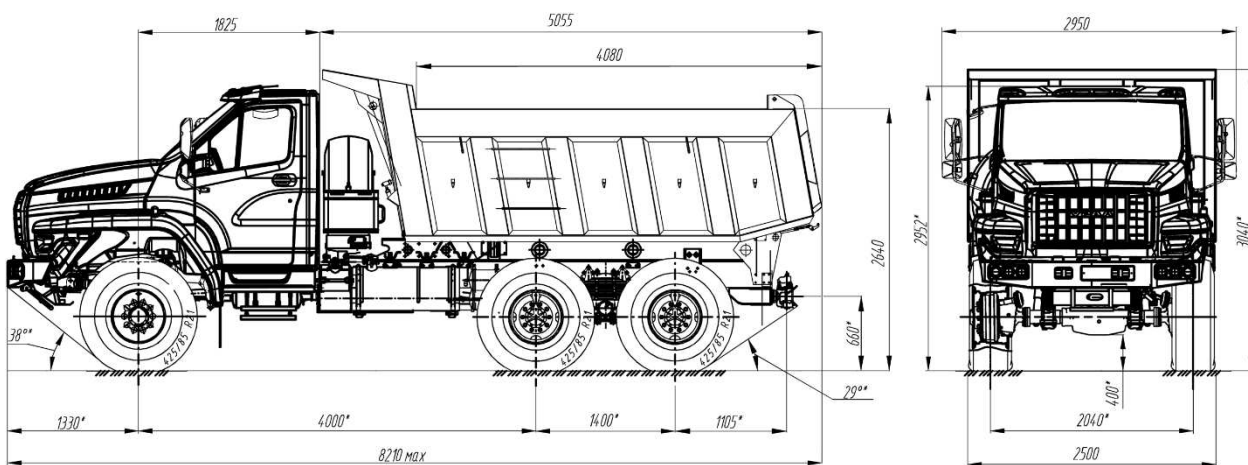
Габаритные размеры автомобиля-самосвала Урал-55571-5121-72/74
